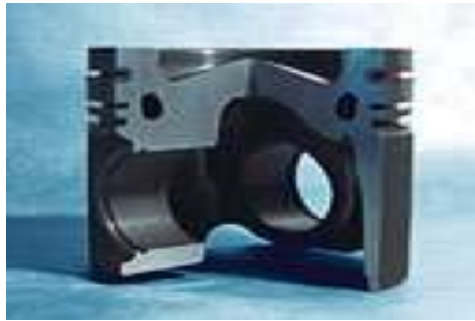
Pistão com segmentos e canal de arrefecimento
